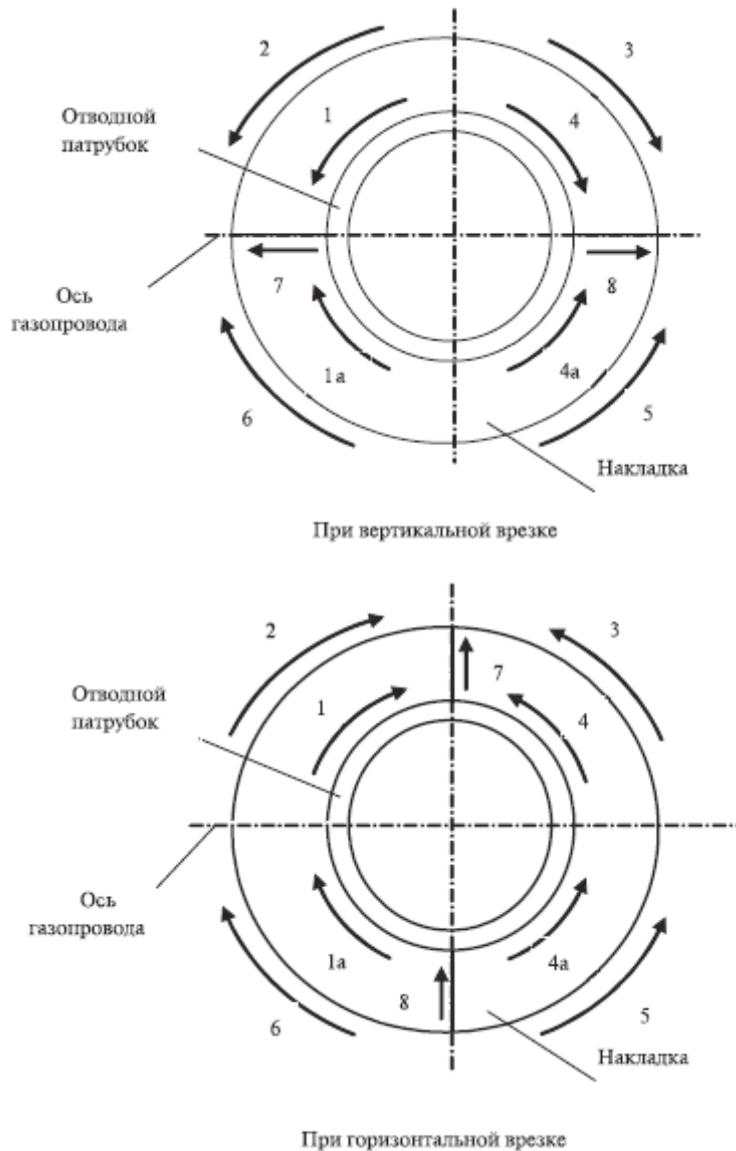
Порядок наложения угловых сварных швов приварки отводного патрубка
